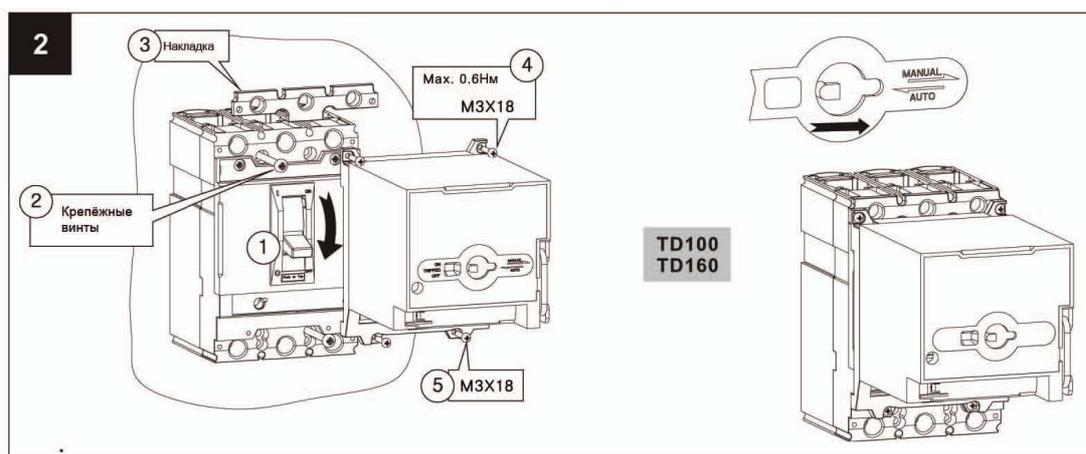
Установка моторного привода на выключатели TD100 и TD160
